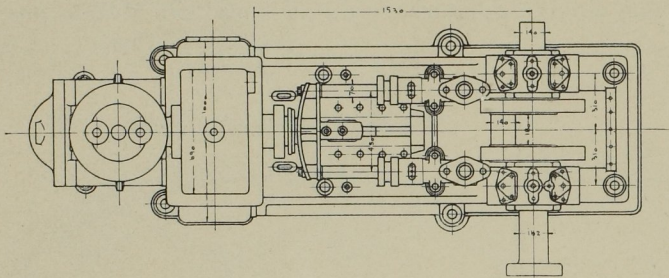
Grundriss der Express-Pumpe. Masst. 1:40.
